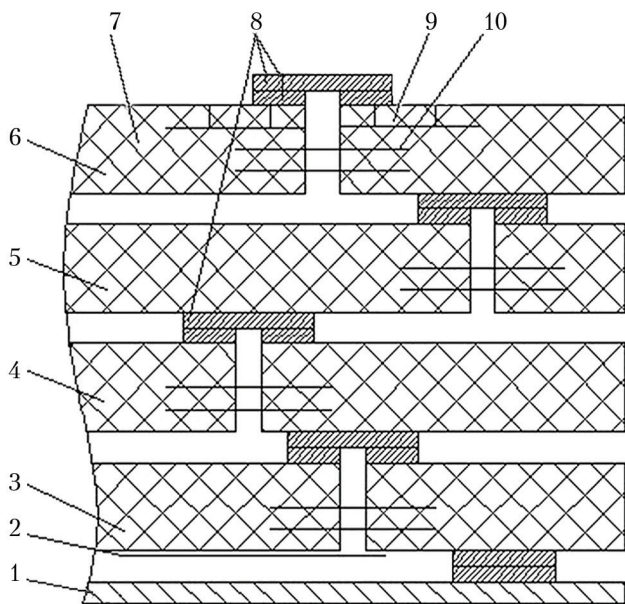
Конструкция мата теплоизоляции марки ЭВТИ-2РЛ: 1 — стенка бака; 2 — выступающий экран; 3–6 — пакеты теплоизоляции; 7 — слои ЭВТИ; 8 — текстильные застежки; 9 — семь общих теплоизоляционных слоев; 10 — экраны для перекрытия зазоров
